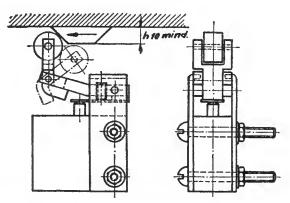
Nockenventil mit Rollenhebel und Leerrücklaufvorrichtung
